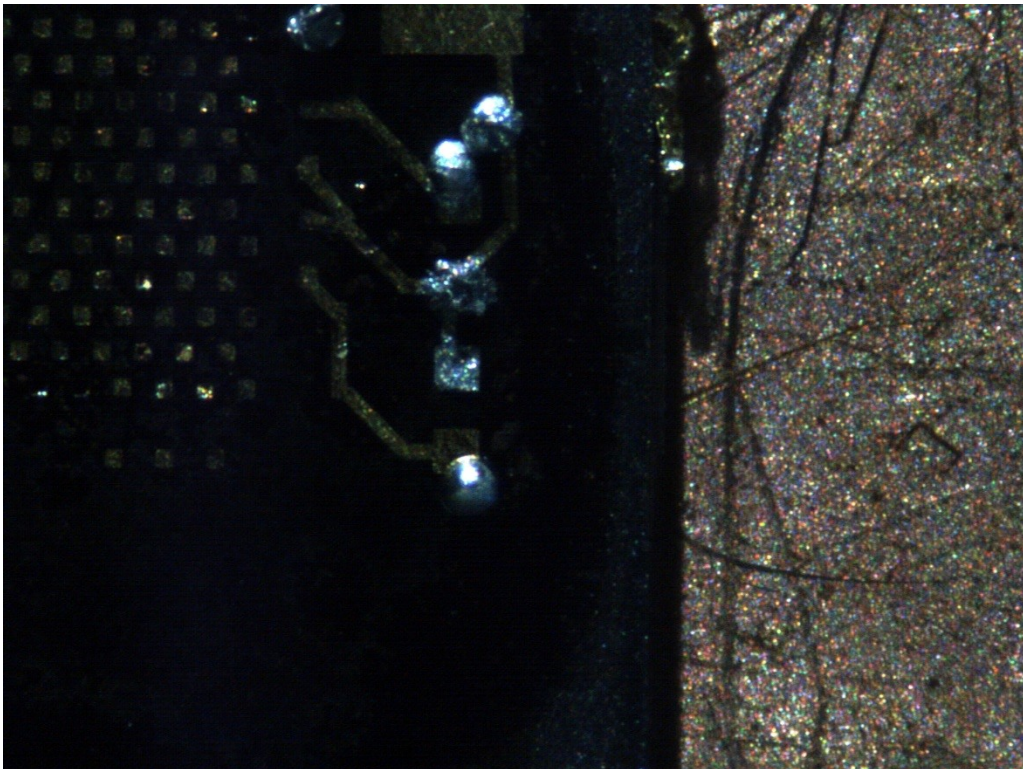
Résultat du *shear test* des billes de soudure pour l'expérience de soudure
